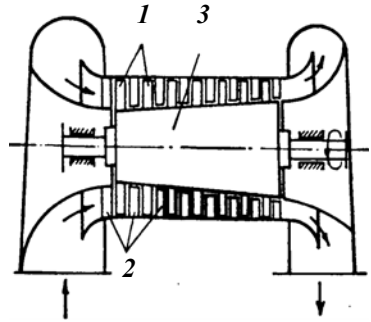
Схема осьового компресора: 1 – робочі лопаті; 2 – напрямні лопаті; 3 – ротор
